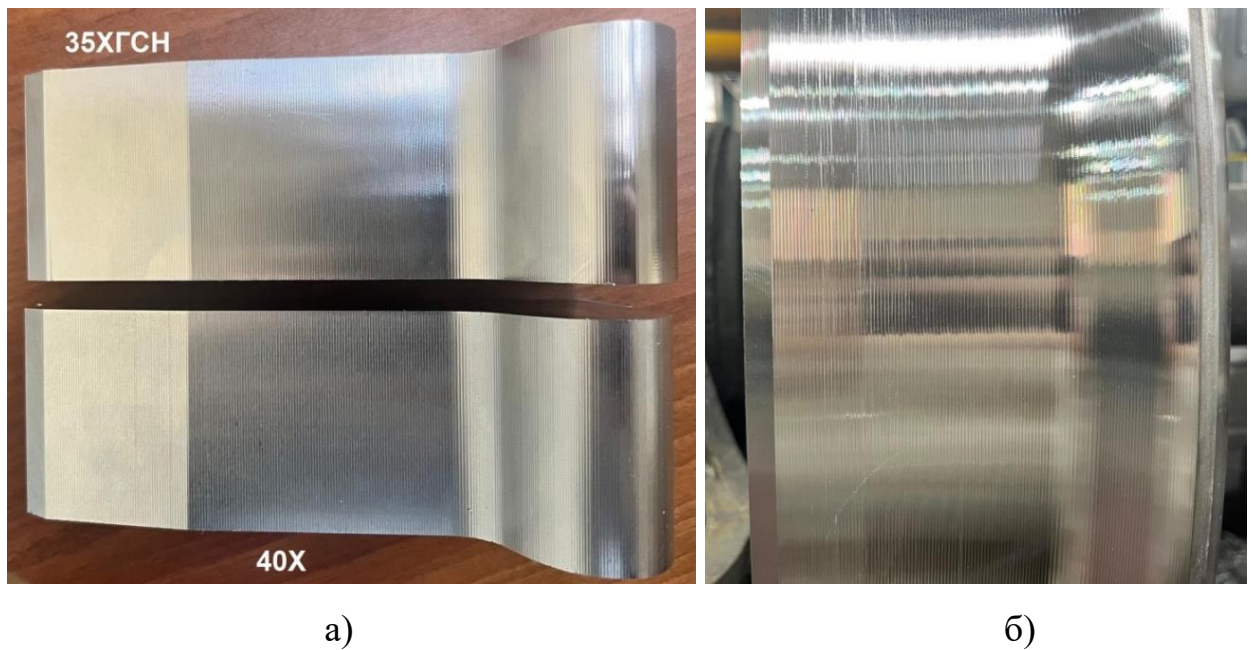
Обработанные поверхности колесных пар: фрезерование дисковой фрезой с СМП (а), точение резцом с СМП (б).
